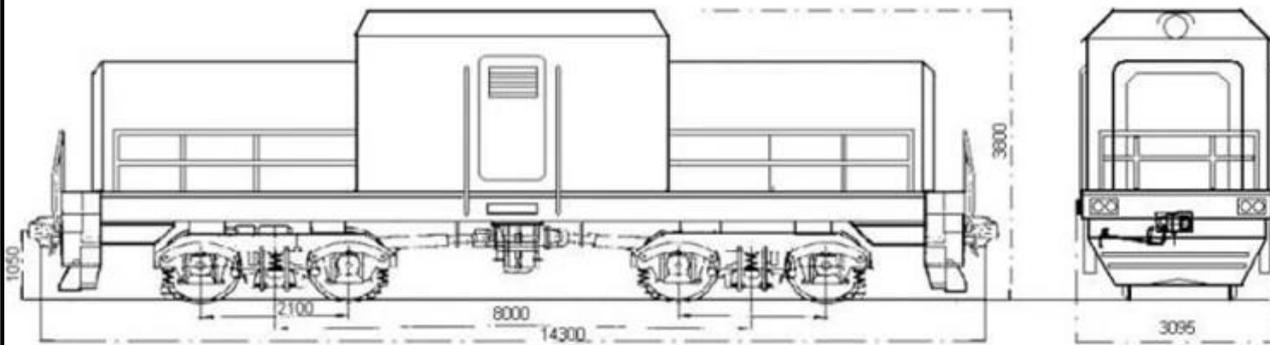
Общий вид вагонотолкателя ВТМ-40У
